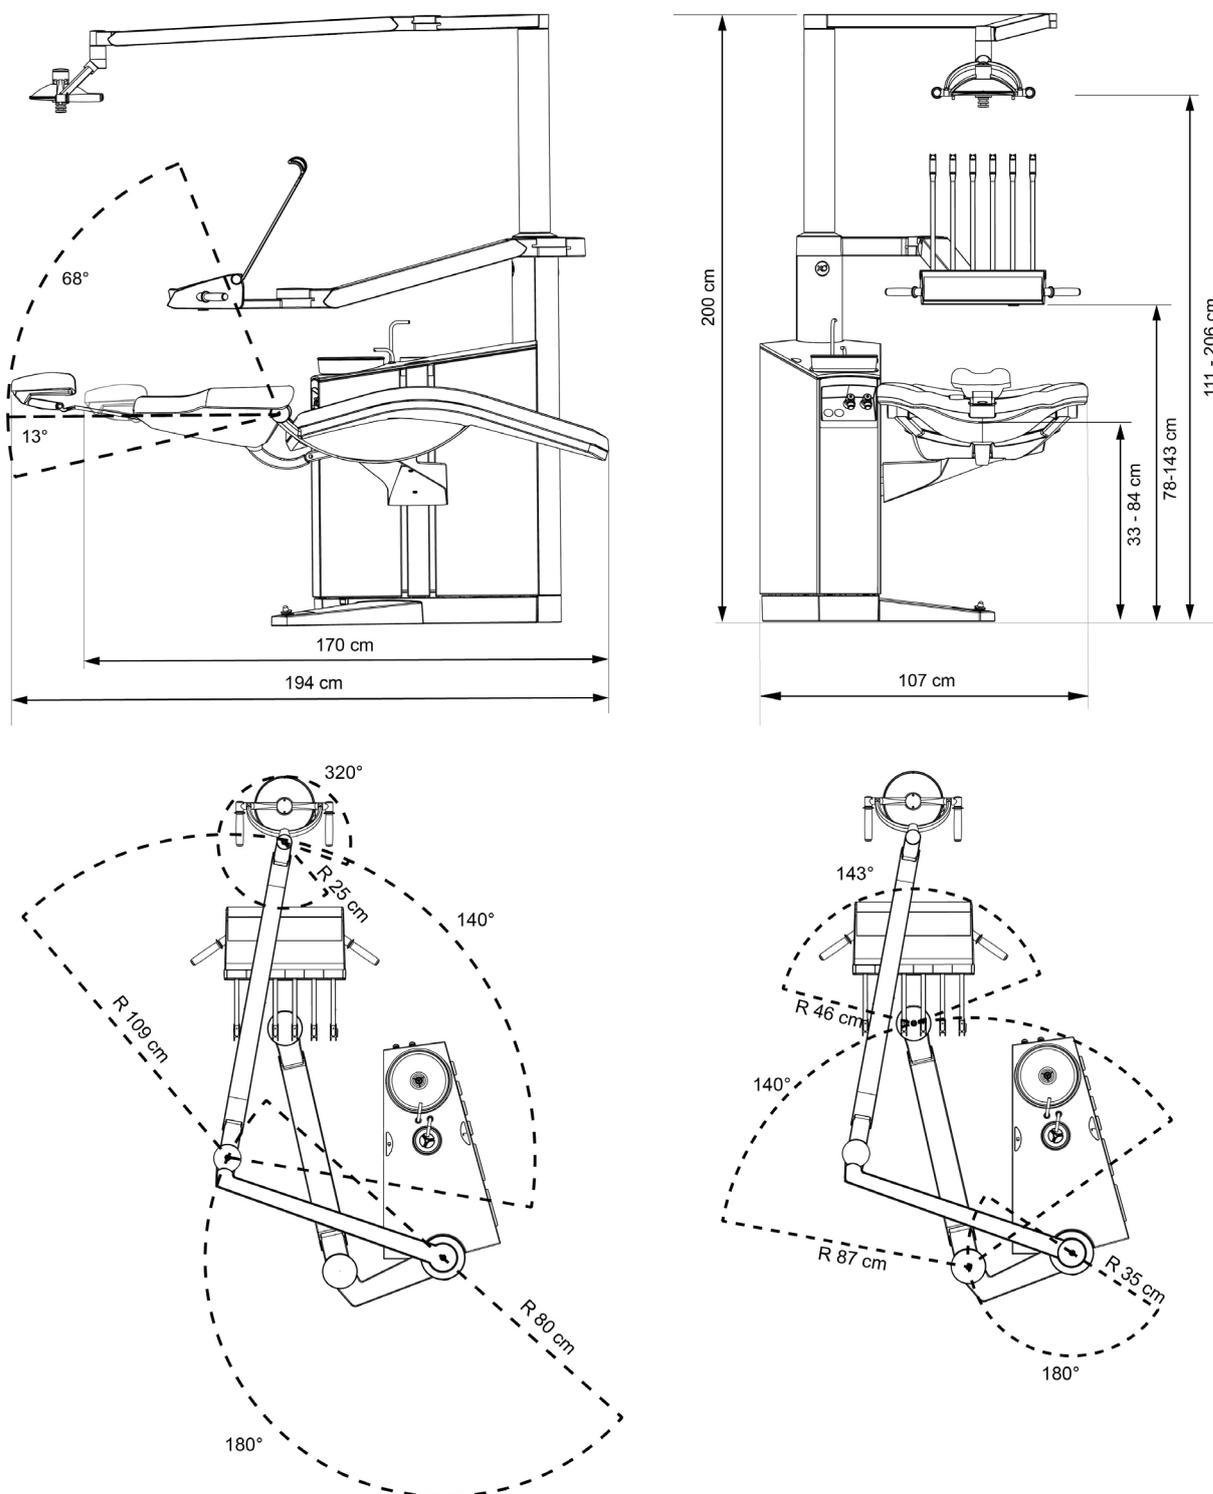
Dimensioni di XO FLEX e ampiezza di movimento
